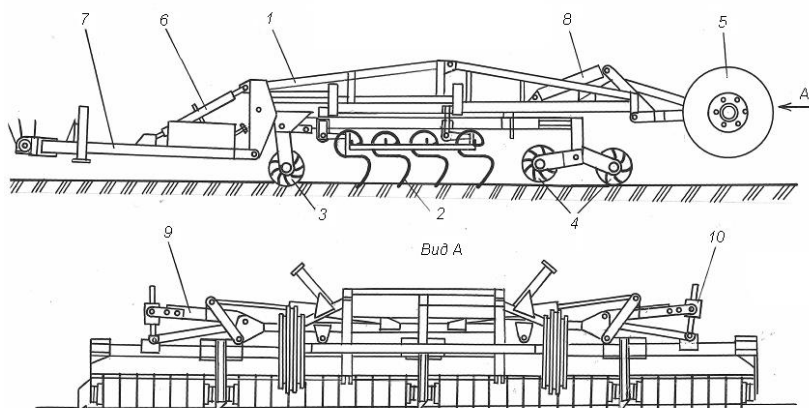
Агрегат комбинированный широкозахватный АКШ-7,2: 1 – рама; 2 – рыхлительные секции; 3 – каток передний; 4 – катки задние; 5 – колесный ход; 6 – талреп; 7 – сница; 8 – гидроцилиндр; 9 – механизм догрузки и подъема боковых секций; 10 – амортизаторы
